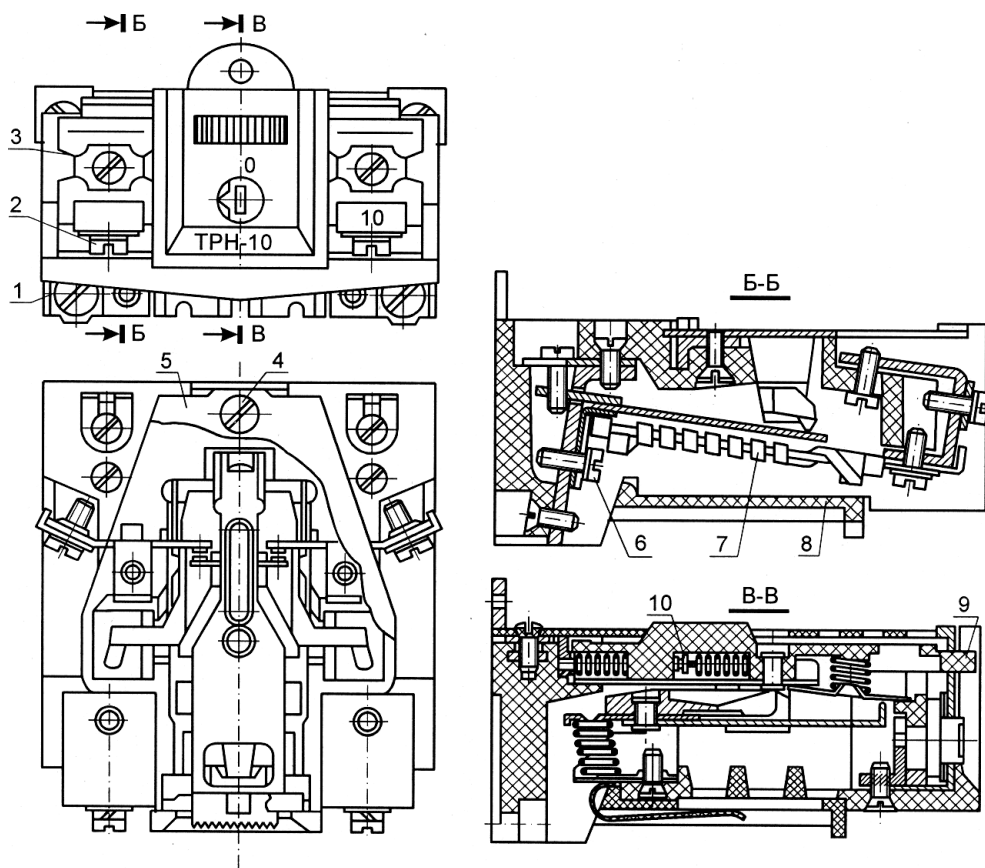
Конструкция теплового реле ТРН-10: 1—6 — винты; 5 — крышка; 7 — нагревательный элемент; 8 — пластмассовая крышка; 9 — шток; 10 — контактный мостик.
